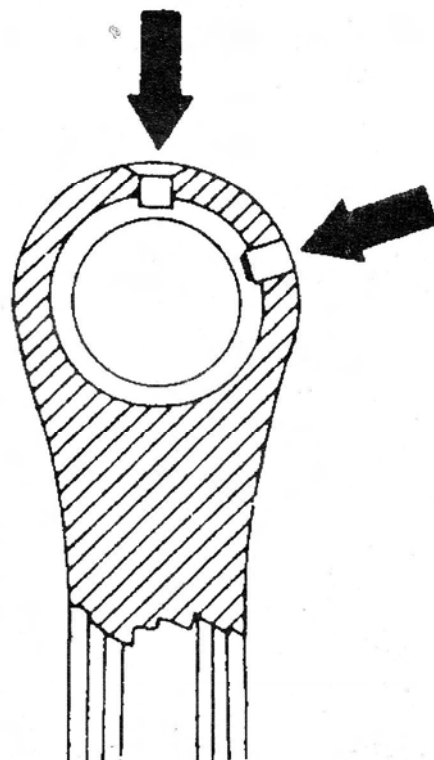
При запрессовке втулки подшипника шатуна обеспечить совпадение смазочных отверстий.
